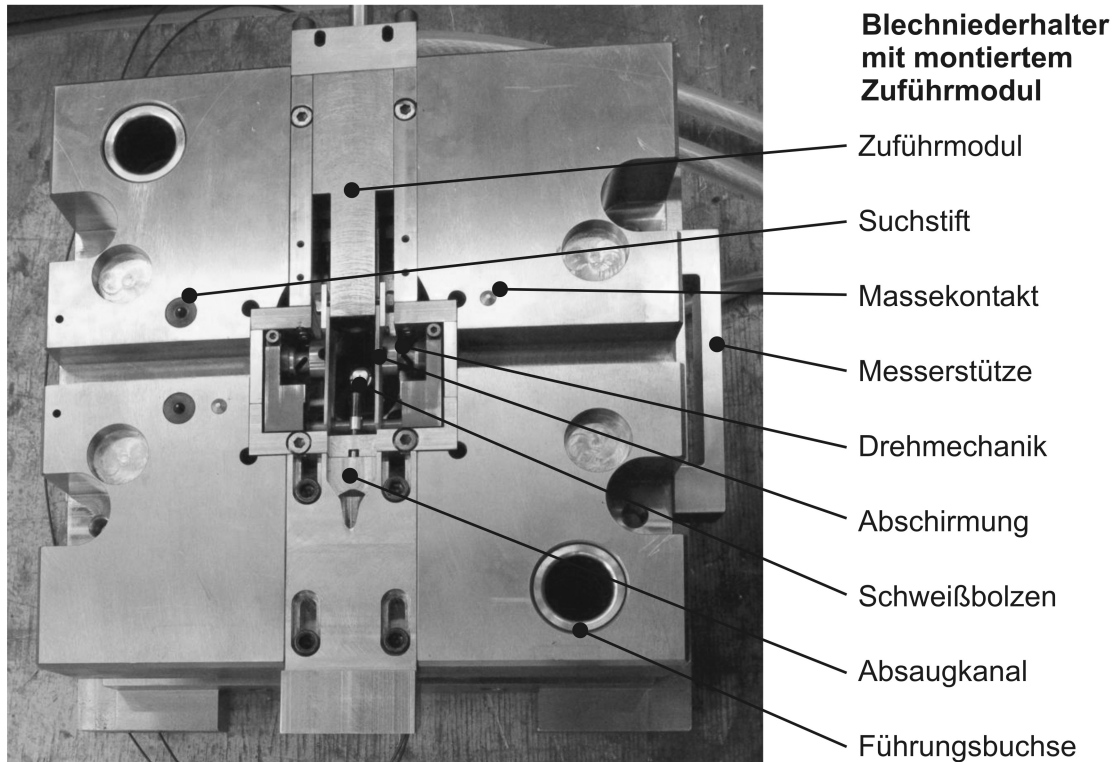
Unterseite des Blechniederhalters mit montiertem Zuführmodul
